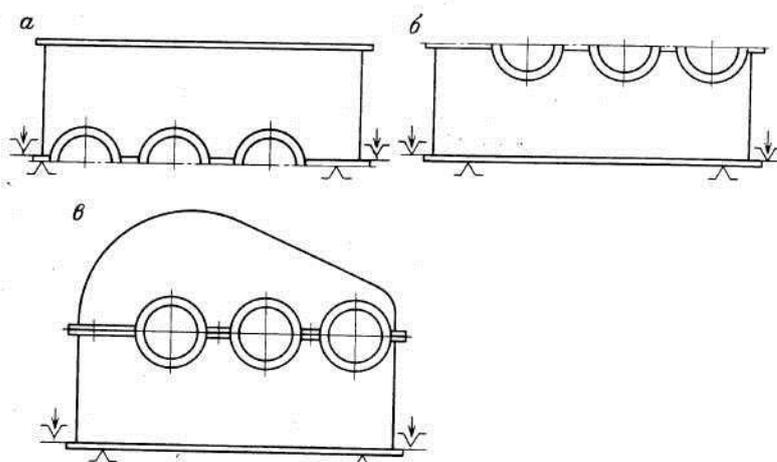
Схемы базирования заготовок корпусных деталей при обработке по черновой (а) и чистовым (б, в) технологическим базам
